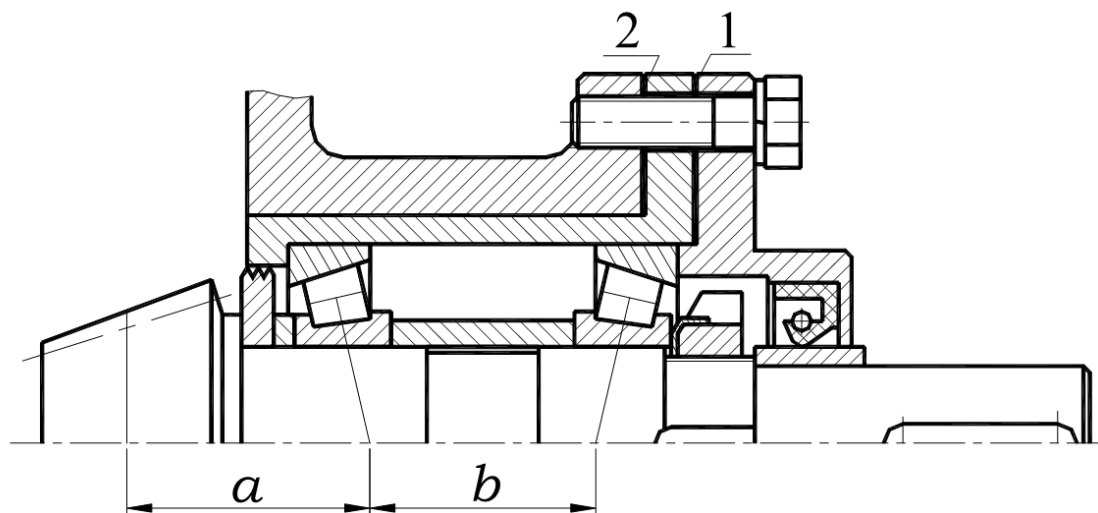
Конструкция узла конической шестерни с радиально-упорными шариковыми подшипниками: 1 – стакан, 2 – корпус.
